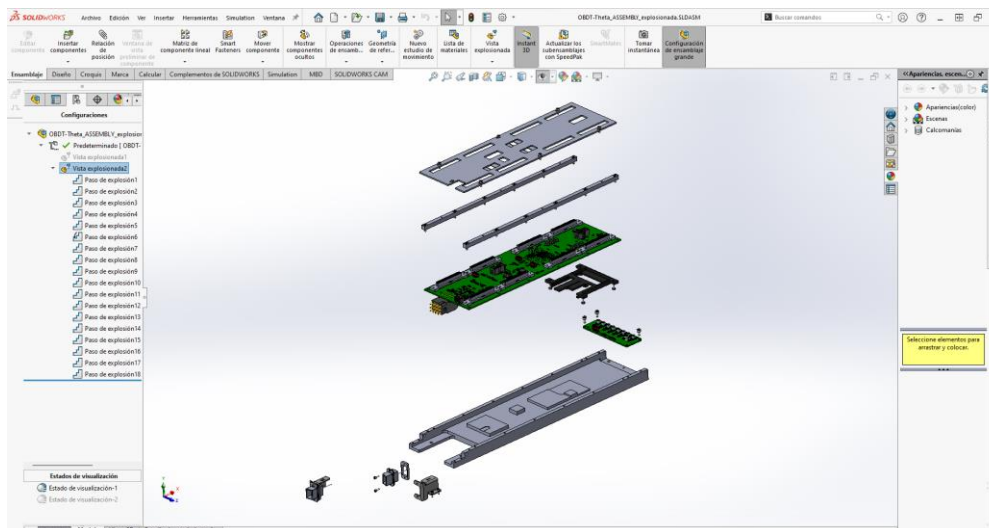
Vista explosionada del ensamblaje 3D de la OBDT-Theta en Solidworks.
